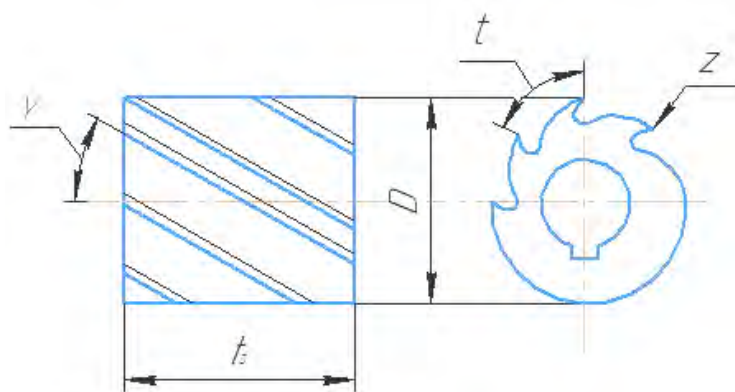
Геометрические параметры осевой цилиндрической фрезы:
